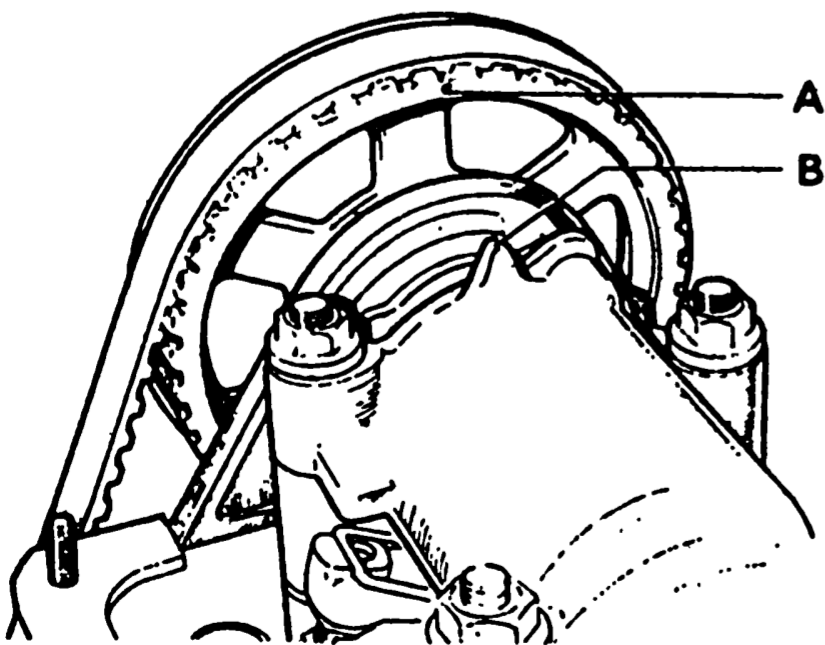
Проверка совпадения установочной метки на шкиве распределительного вала с меткой на корпусе подшипников: А - метка на шкиве; В - метка на корпусе подшипников
